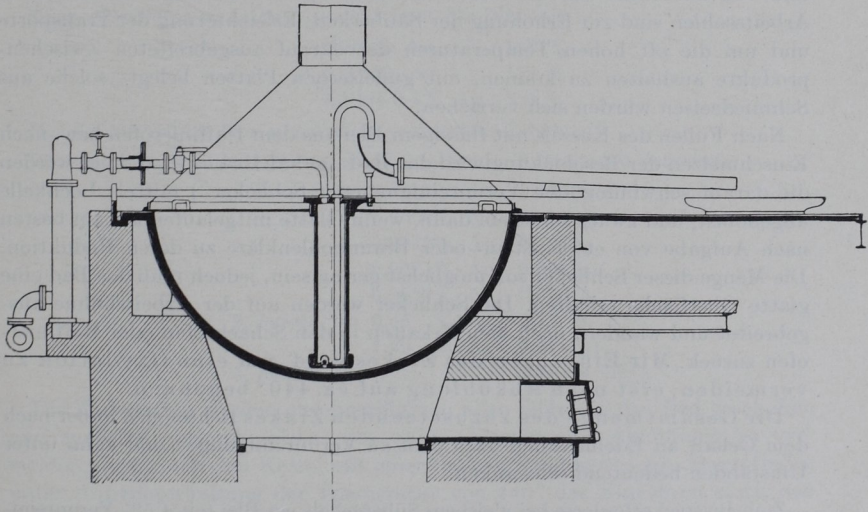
Entsilberungskessel mit Rösingscher Bleipumpe.
